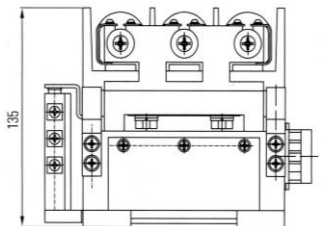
Габаритные размеры КВТ-1,14-80/125/160
